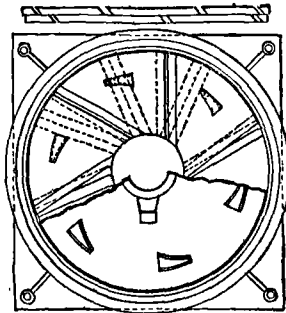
Chaudière de Mac Cone ; coupe horizontale.
